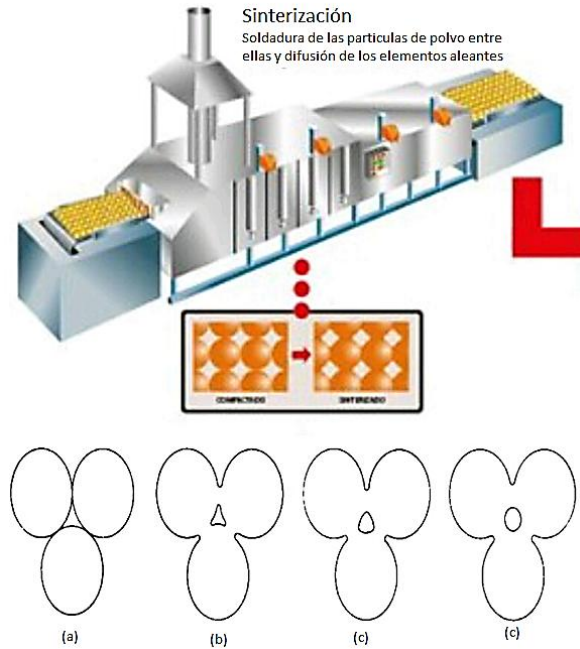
Soldadura de las partículas de polvo entre ellas y difusión de los elementos aleantes.⁷
